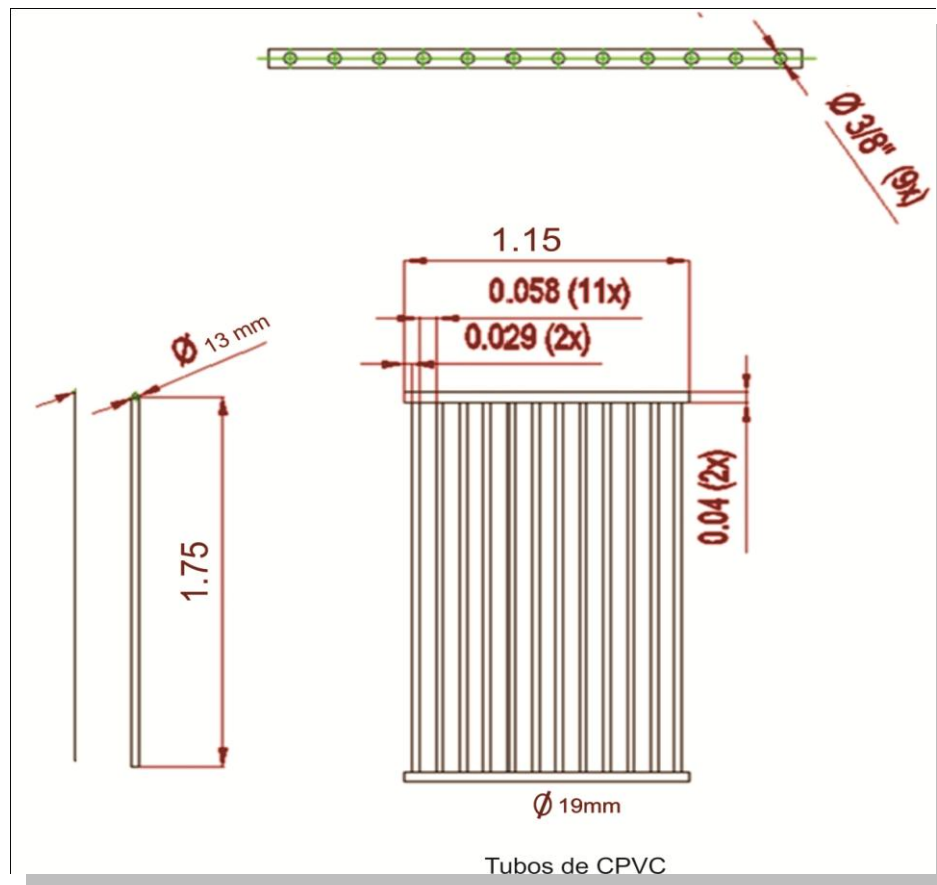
HERNANDEZ REYES – 2011 - Dimensiones del Serpentin.
